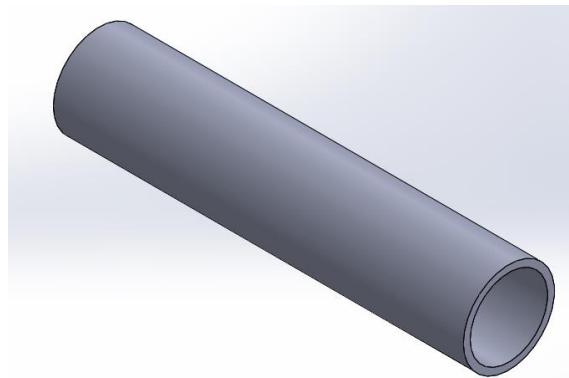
Casquillo largo de la máquina de arrastre M-10 de BMM.
